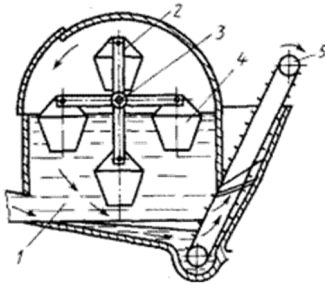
Роторна установка: 1 – ванна, 2 і 4 – контейнери, 3 – вал приводу; 5 – очисний пристрій
